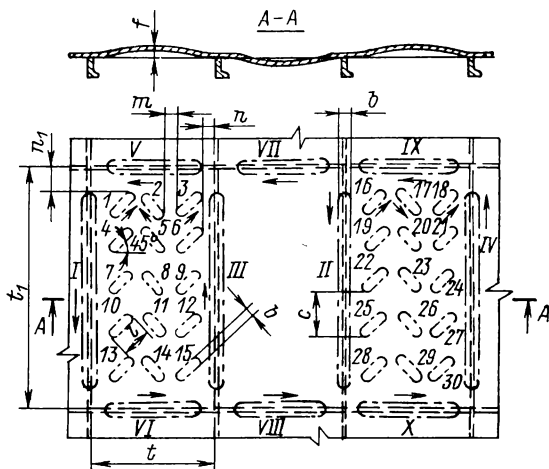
Схема нагрева при выполнении правки обшивки с перекрестным набором.
